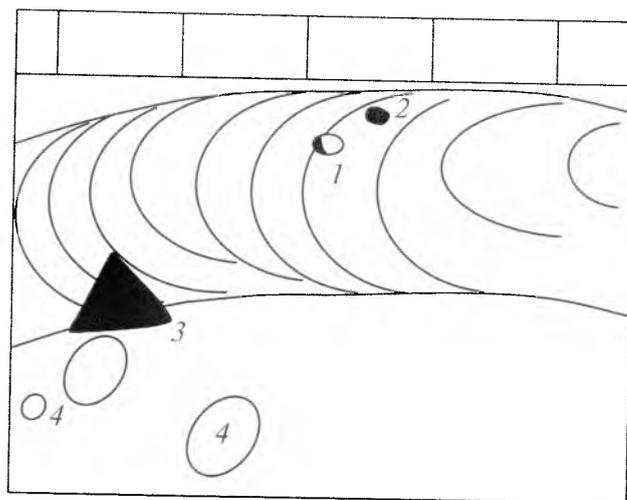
Пора 1 (газовая полость округлой формы) в стыковом сварном соединении трубопровода. Наблюдаются также шлаковое включение 2, не удаленный шлак 3, брызги металла 4
